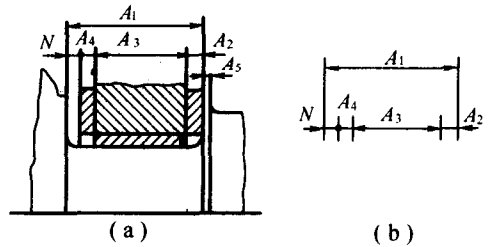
曲轴主轴颈与止推轴承配合及轴向尺寸的尺寸链
